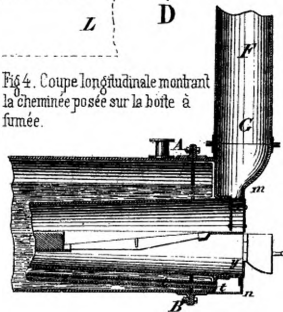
Coupe longitudinale montrant la cheminée posée sur la boîte à fumée.
